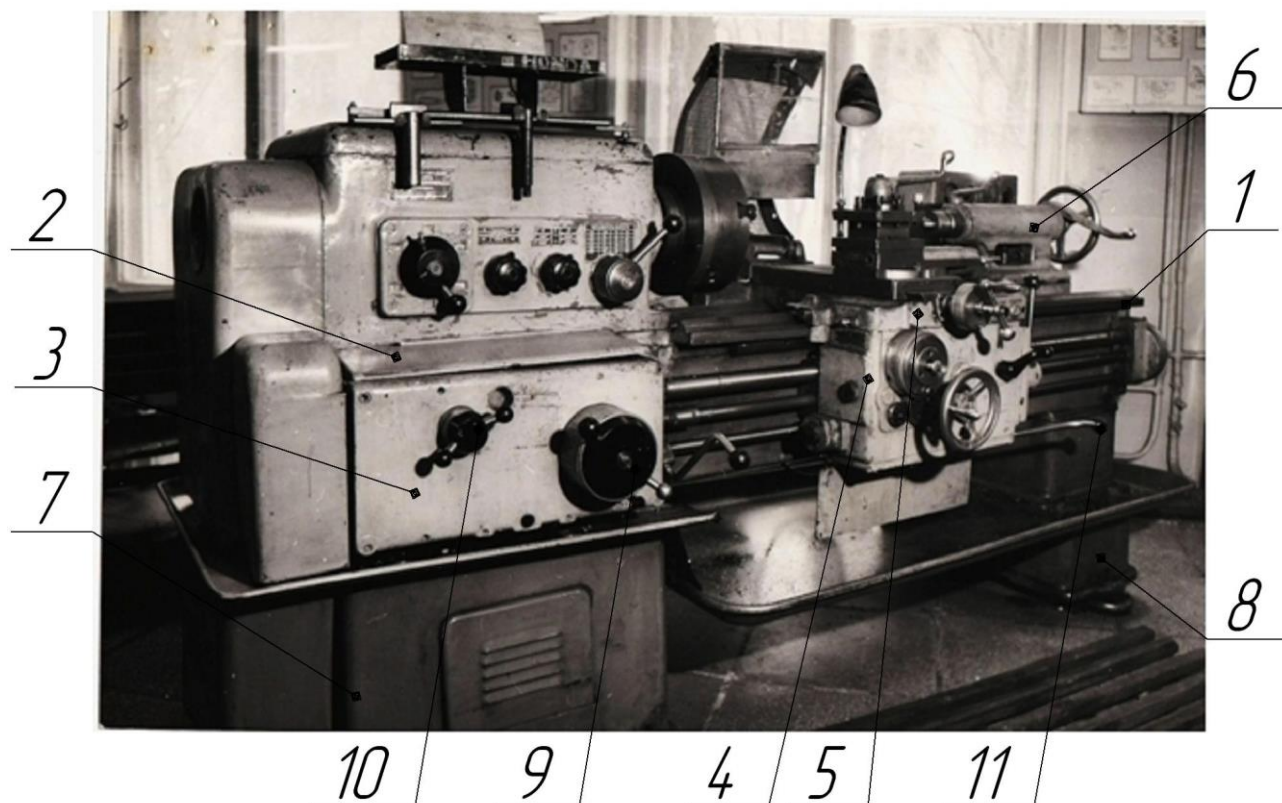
Общий вид станка: 1 – станина, 2 – передняя бабка, 3 – коробка подач, 4 – фартук, 5 – суппорт, 6 – задняя бабка, 7 – левая тумба, 8 – правая тумба, 9 – рукоятка выбора шага резьб или подач, 10 – рукоятка включения винта напрямую и установка вида резьбы, 11 – рукоятка управления шпинделем
